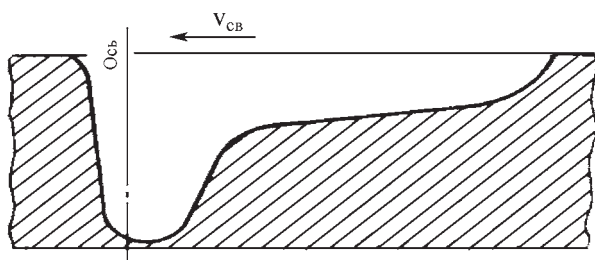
Форма сварочной ванны в продольном сечении
